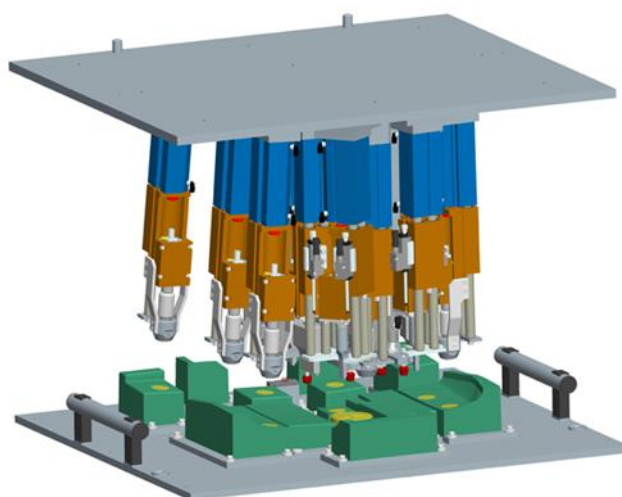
Установка для сварки фирмы HerrmannUltrasonic
